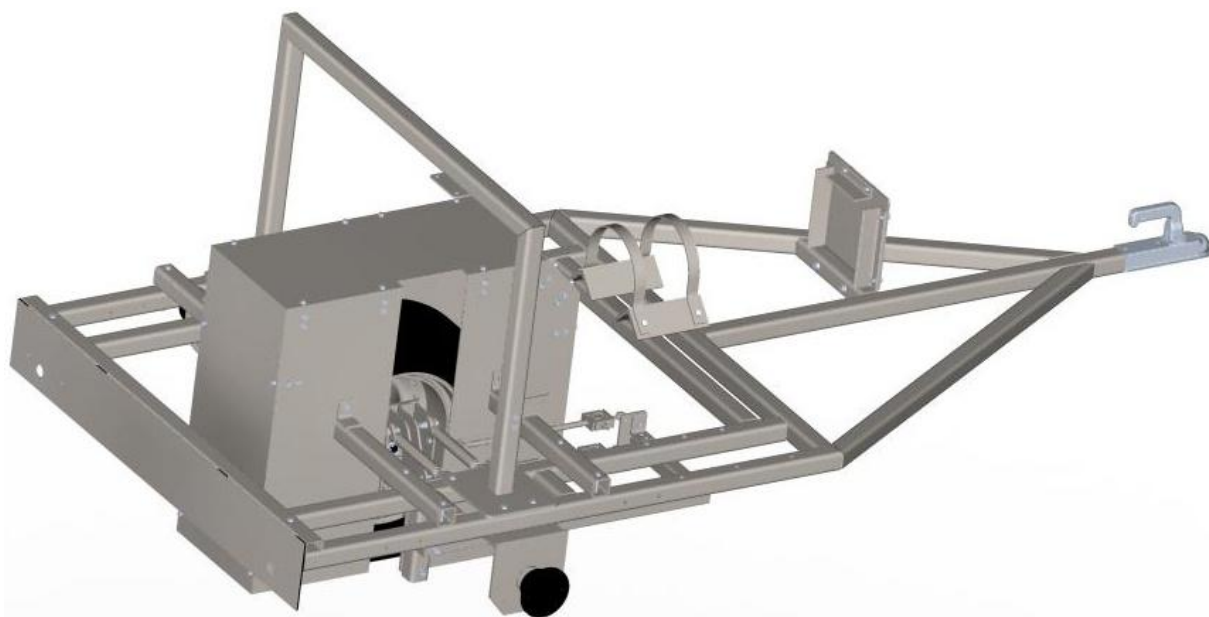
Model krytu kola s měřenou pneumatikou (pohled zleva)
